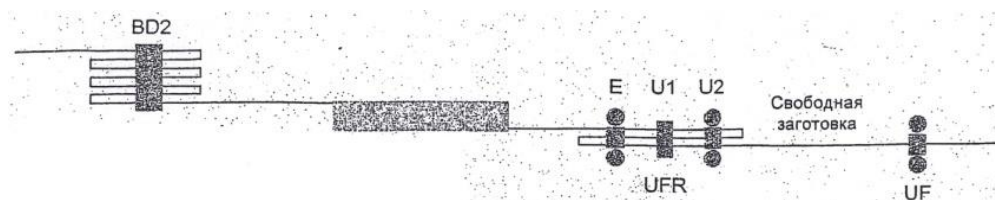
Типовая схема калибровки для прокатки рельсов
